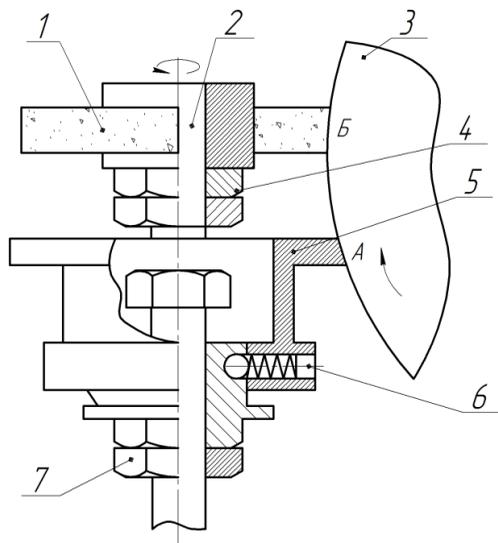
Устройство для регулирования глубины врезания абразивного круга: 1 – шлифовальный круг; 2 – шпиндель; 3 – отливка; 4, 7 – гайки; 5 – кулачок; 6 – фиксатор
